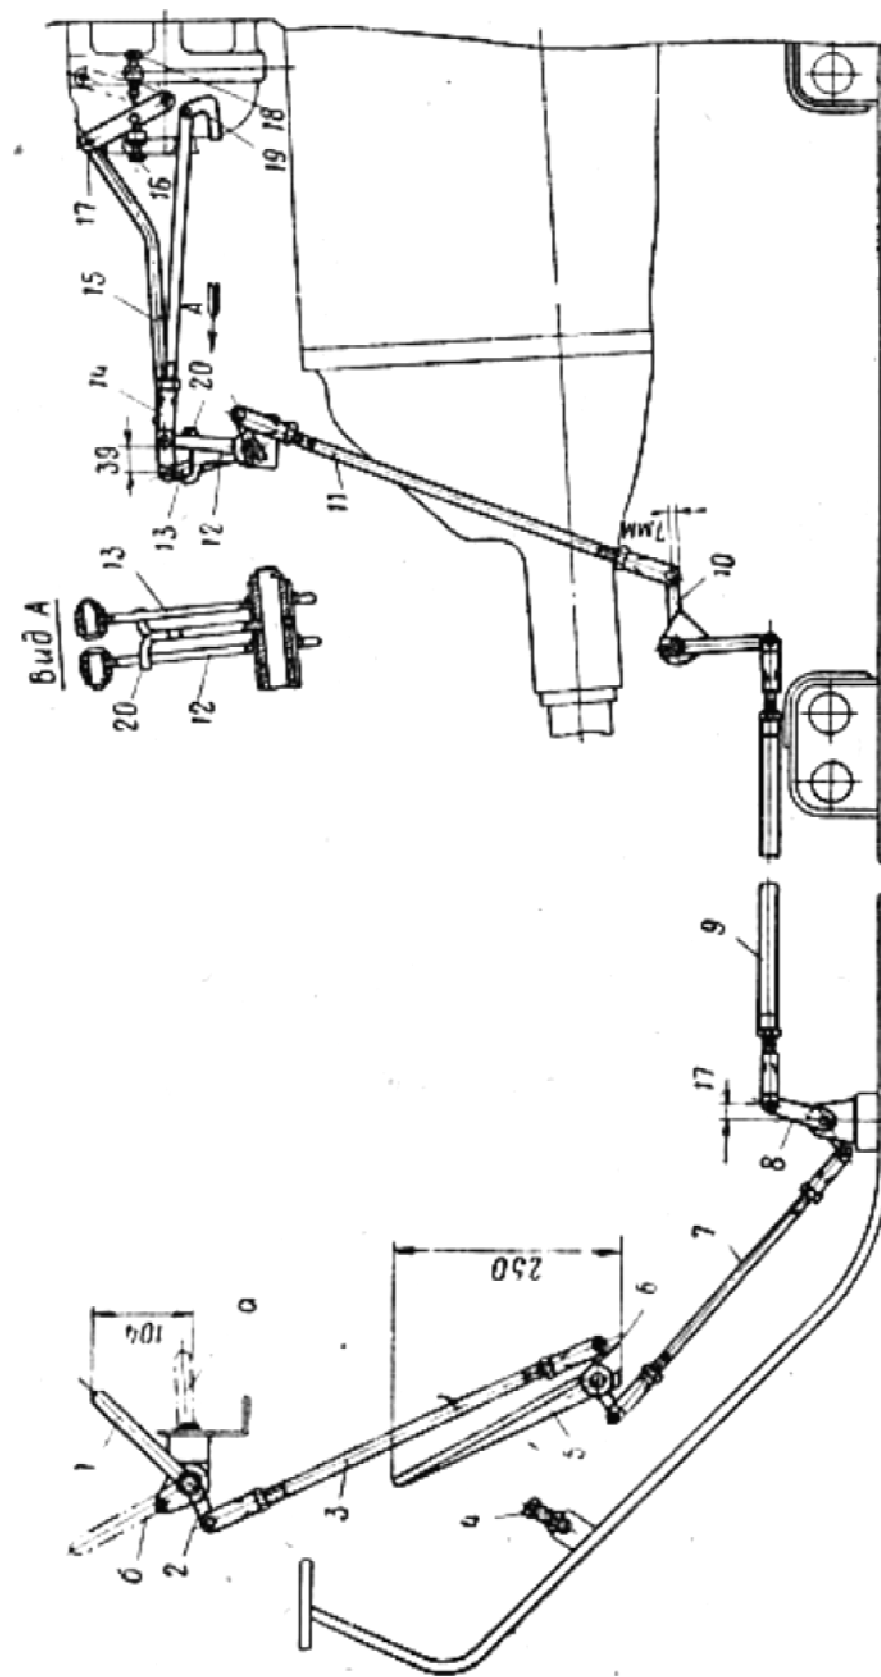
Монтажная схема регулировки привода управления двигателем транспортера-тягача МТ-Л:
